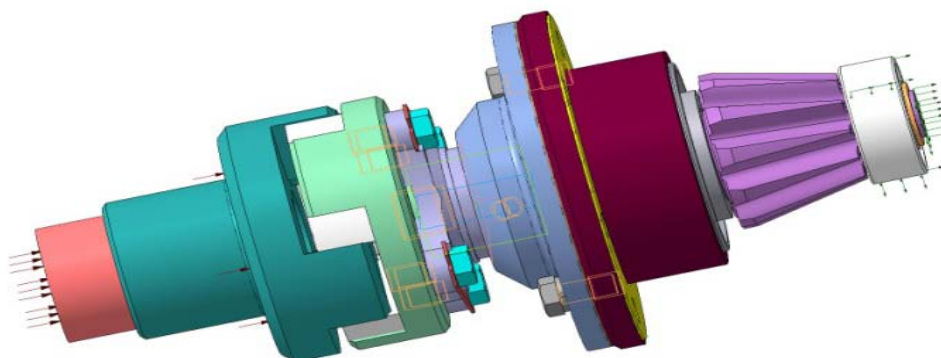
Ведущий вал первой ступени мотор-редуктора
